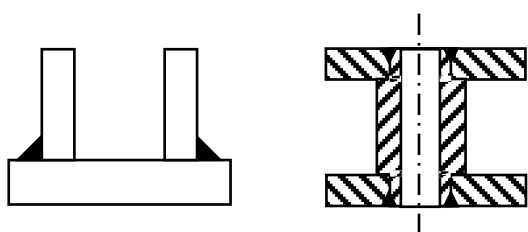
Конструкции удобные для сварки: *a* – швы разнесены; *b* – швы вынесены на поверхность
